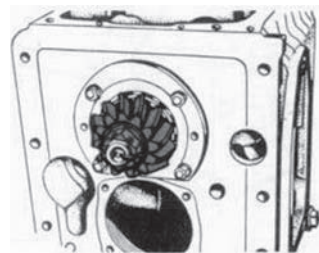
Снятие ведущей шестерни главной передачи для ее замены или регулировки ее установочной высоты
